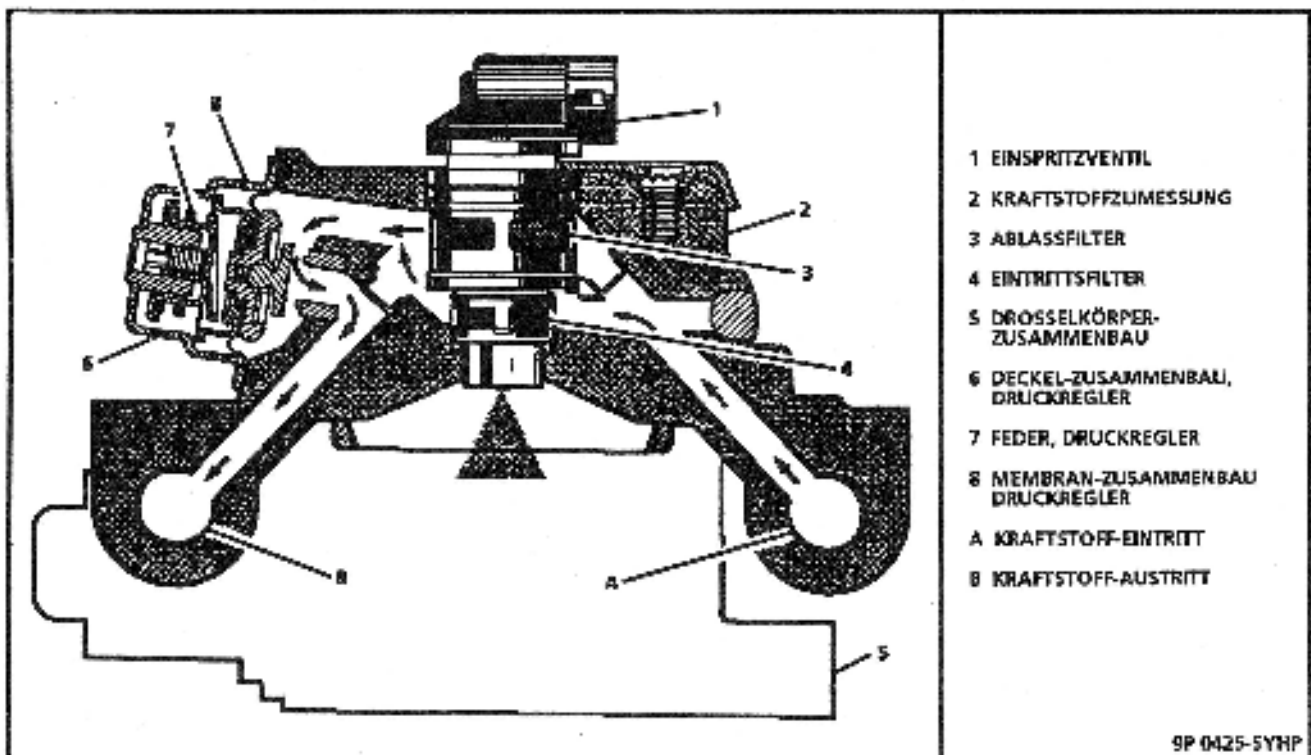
Kraftstoffzumessung mit Einspritzventil und Druckregler
